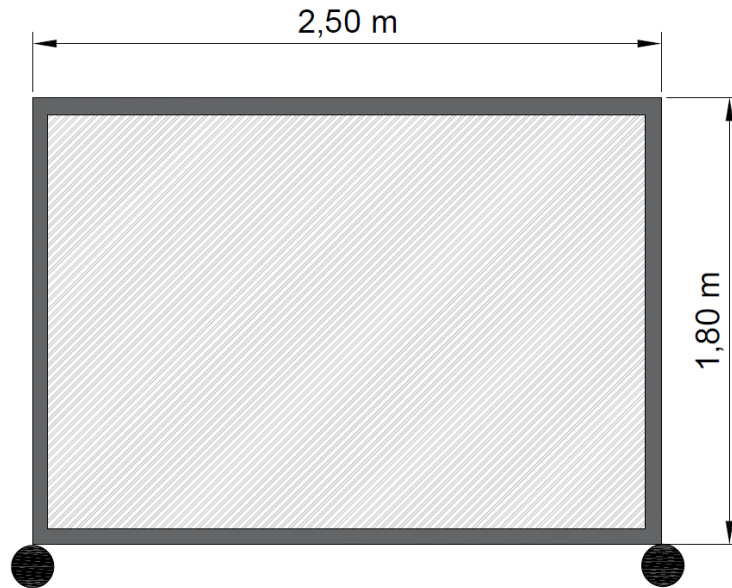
Vista frontal del apantallamiento térmico para la zona de puente grúa de la propuesta 1
